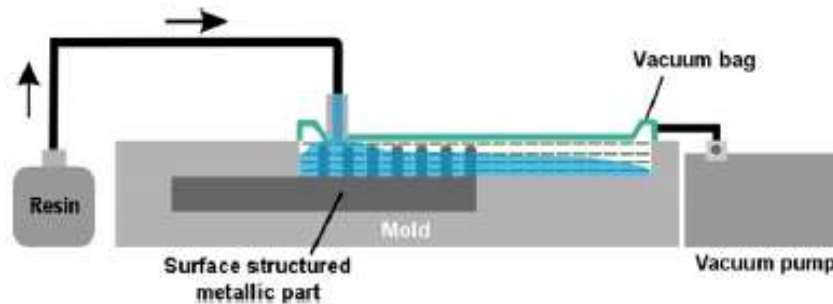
(Feistauer, et al., 2019) Esquema del montaje metal-CFRP mediante RTM
